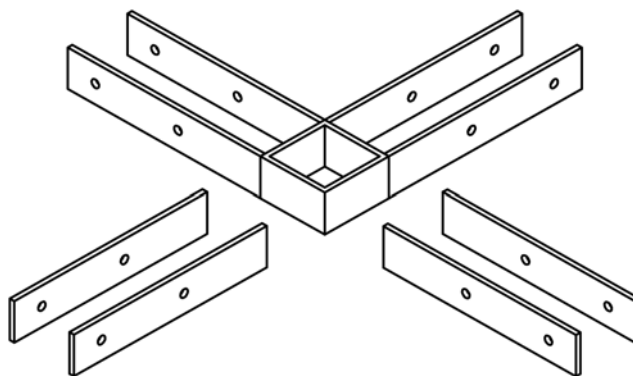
Схема изготовления соединительного сварного элемента
